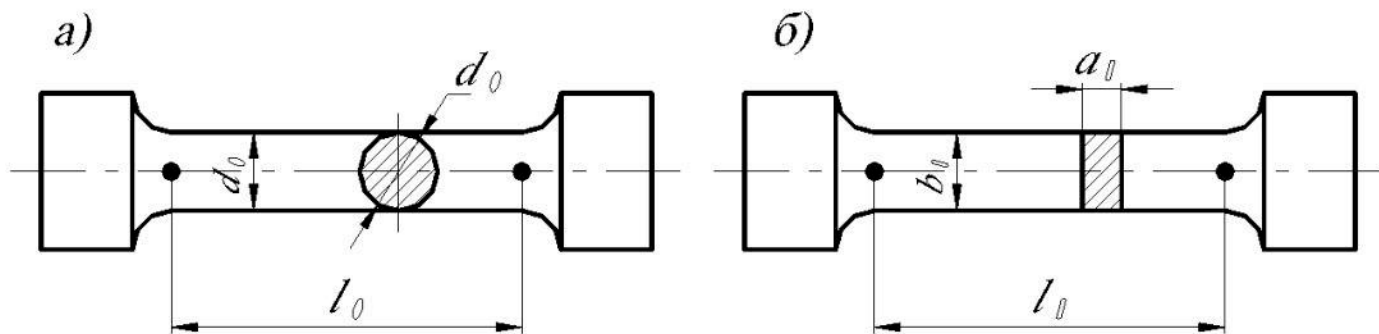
образцы для испытаний на разрыв: а – круглый; б – плоский
